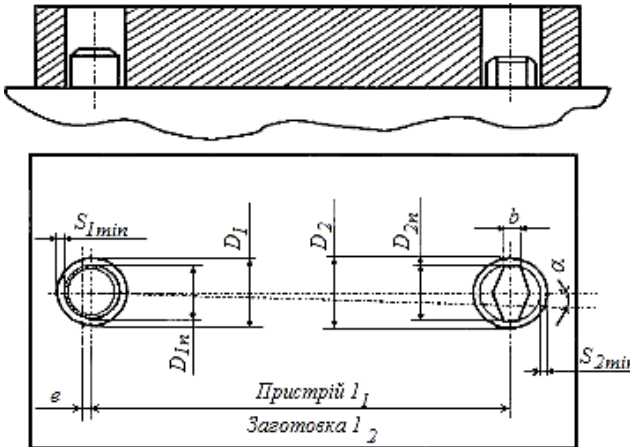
Базування заготовки двома отворами на циліндричний та зрізаний пальці [2]
